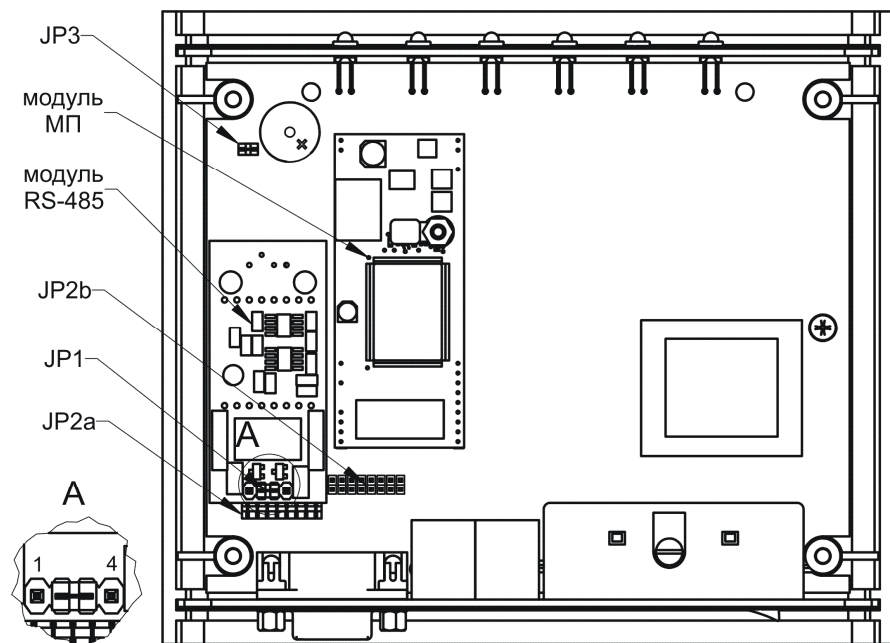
а. Общий вид модема STF/Axxxx/xx5 со снятой верхней крышкой
